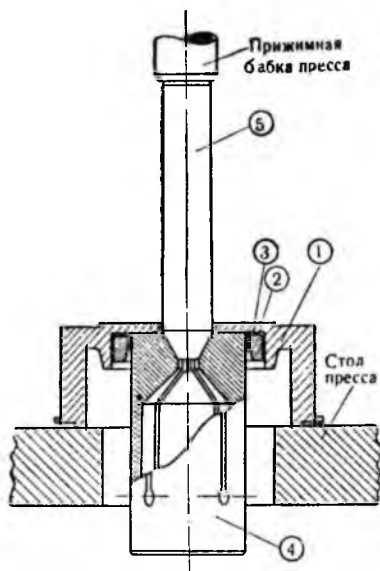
Приспособление для выпрессовки наружных колец шарикоподшипников магнето СС-4 на прессе.
